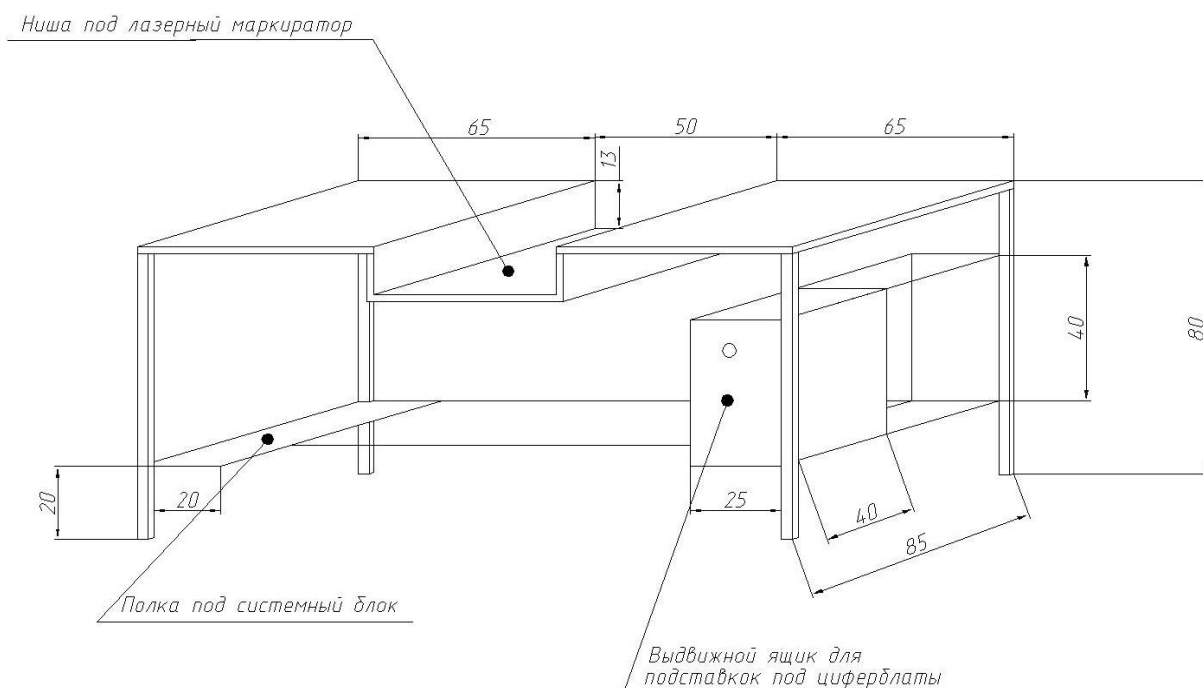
Рабочий стол оператора лазерного маркиратора
